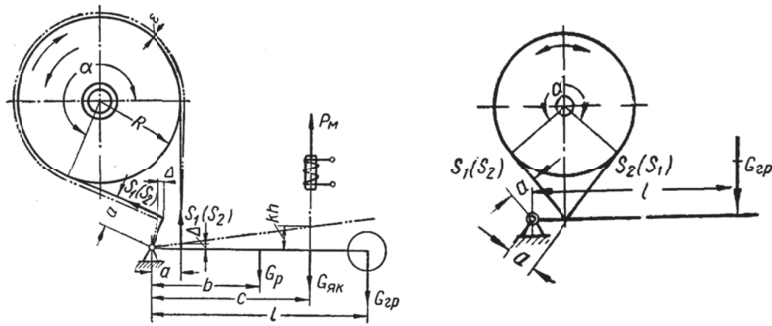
Схемы устройства суммирующего ленточного тормоза
